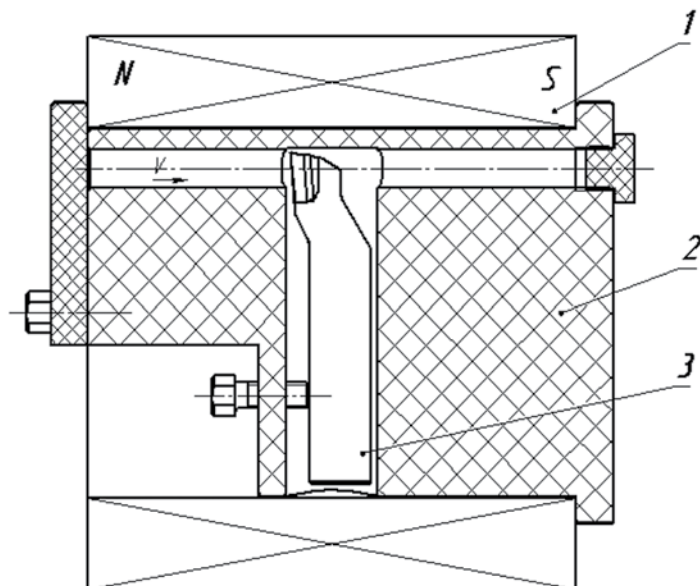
Схема МАП режущей кромки резца (сечение, вид сверху): 1 – магнитно-импульсная катушка (индуктор); 2 – оправка; 3 – резец.
